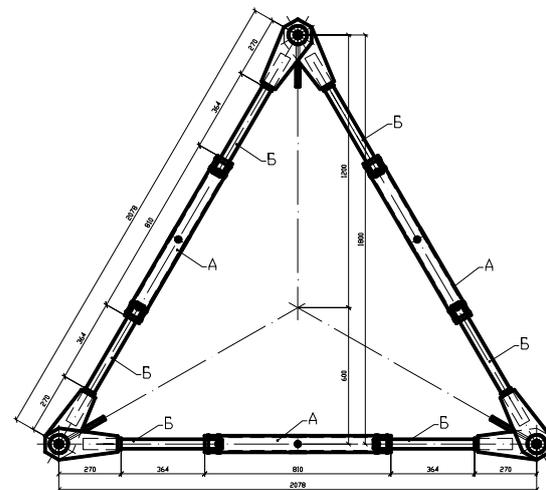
Стенд УУ-ВСК (вид сверху)
